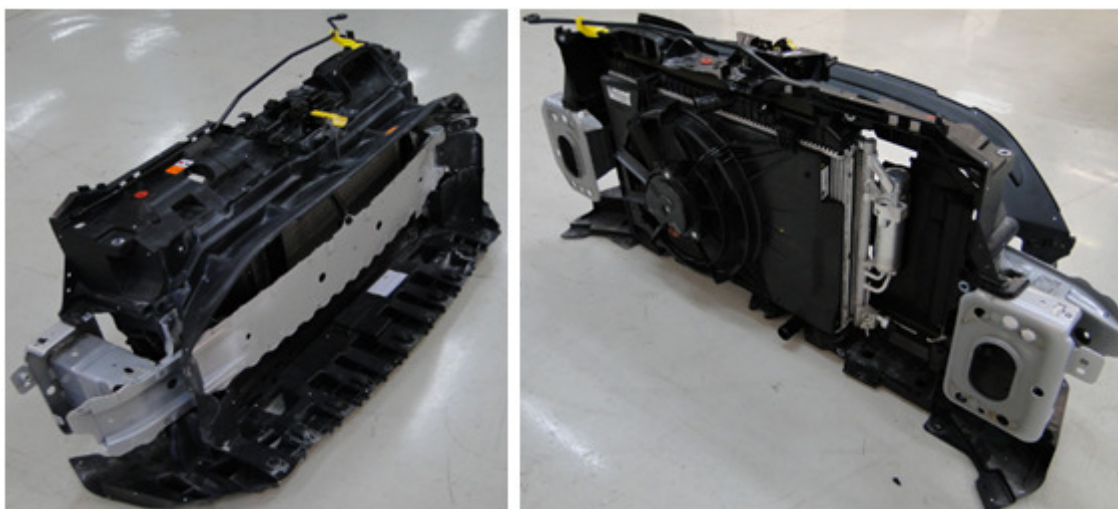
Conjunto modulo frontal. Fonte: O autor (2014).
